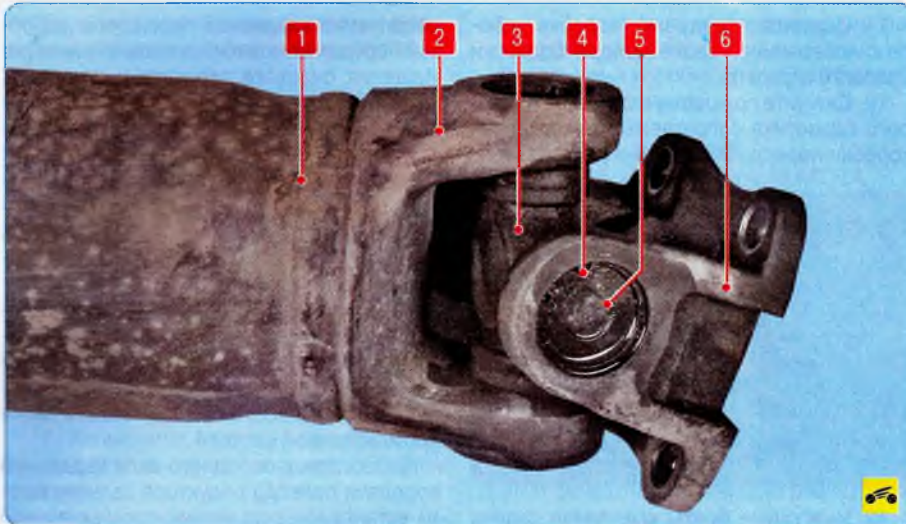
Карданный шарнир: 1 – труба вала; 2 – вилка вала; 3 – крестовина; 4 – стопорное кольцо; 5 – корпус игольчатого подшипника; 6 – задняя вилка
